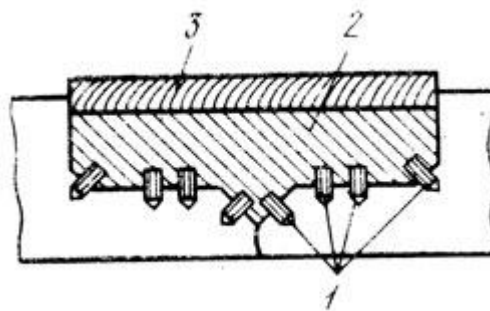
Подготовка чугунного изделия к холодной сварке со стальными шпильками: 1 - стальные шпильки, 2 - стальная связь, 3 - наплавка медно-никелевым электродом
